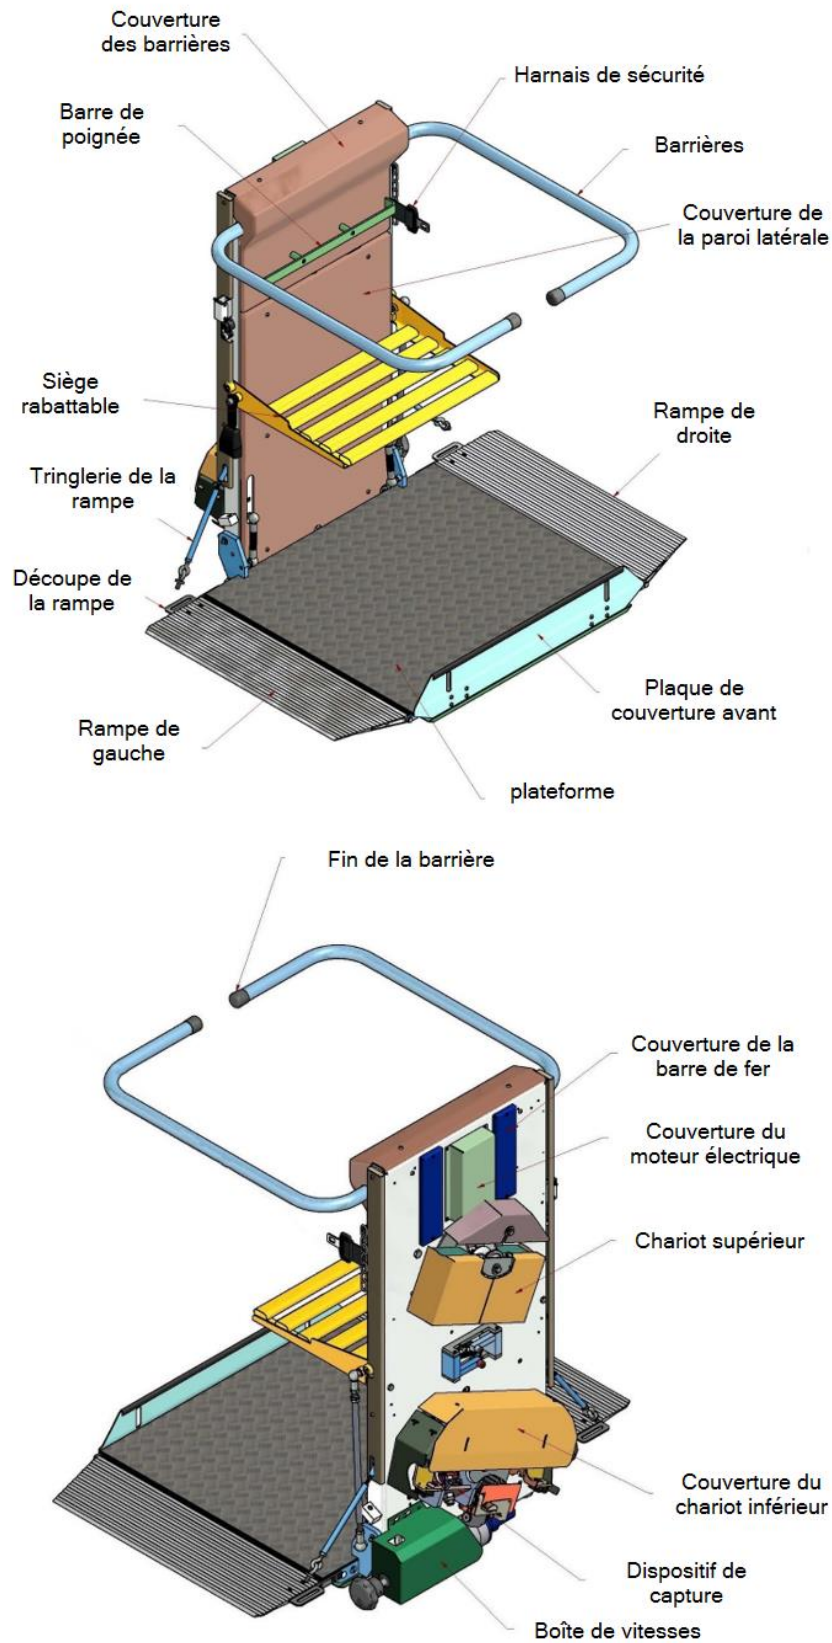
Vue d'ensemble des composants de la plateforme
